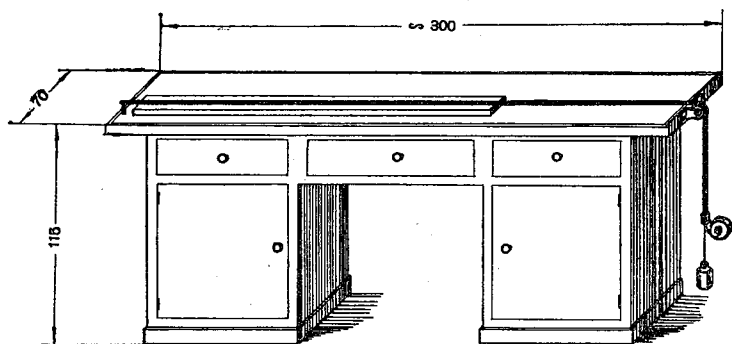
Стол-верстак для поверки реек, штанг и шаблонов.
